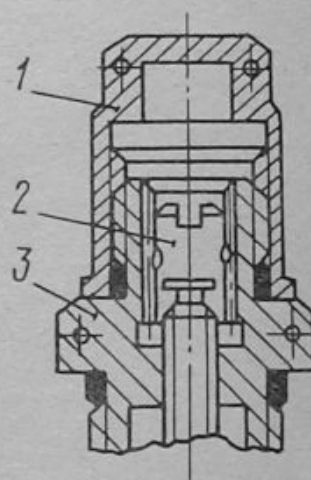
Регулировочный винт № 5 агрегата АТП в сборе:
